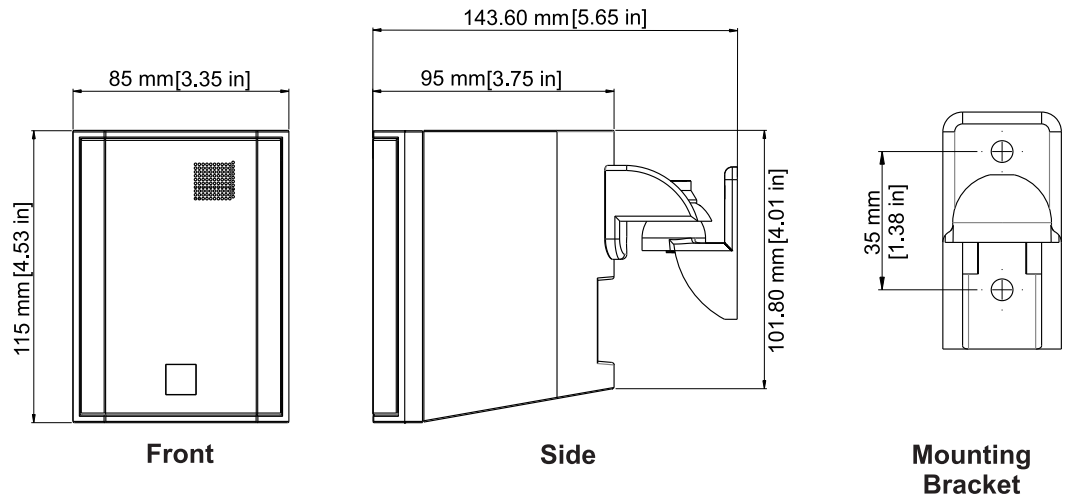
Dimensioni di EVID 2.1 e della staffa di montaggio
